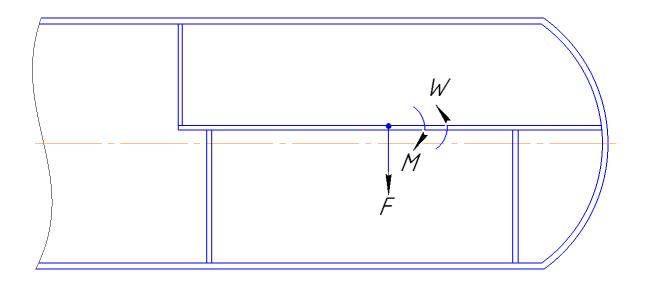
Расчетная схема сварного шва опоры короба к полотну
